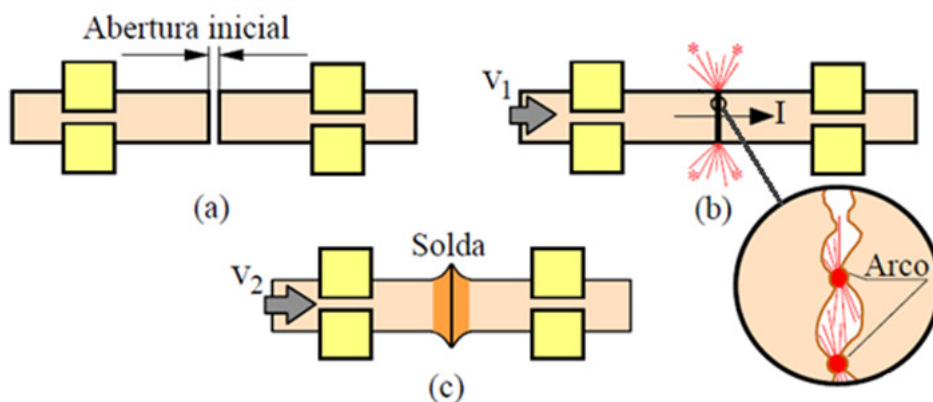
Etapas do processo de soldagem *Flash Welding*<sup>(16)</sup>.
